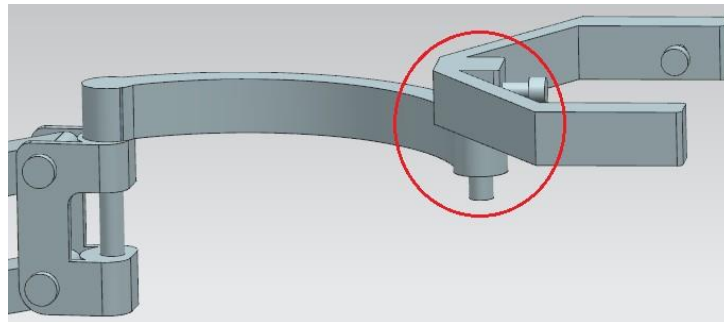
Ensamblaje final de halo con el resto del dispositivo.
